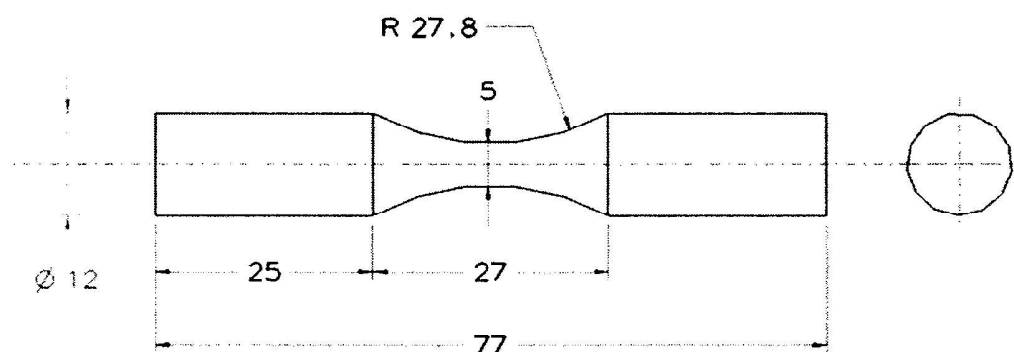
Geometria dos corpos de prova usinados e polidos, que foram testados nos ensaios de fadiga utilizando a técnica de flexão rotativa. As medidas são em milímetros.
